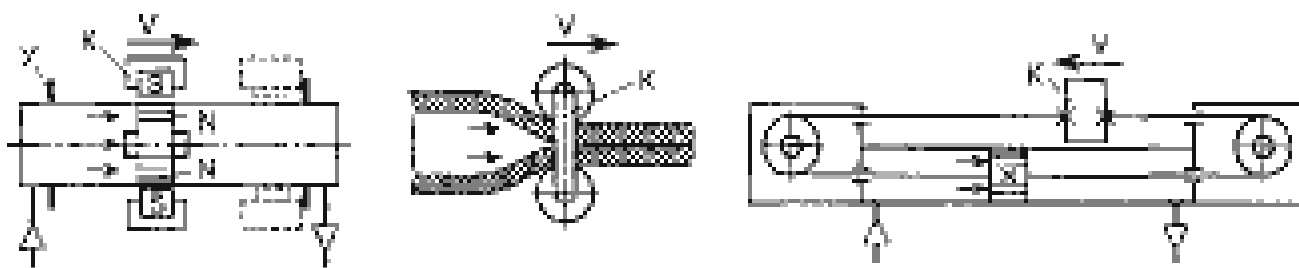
Схемы бесштоковых пневмодвигателей поступательного движения
